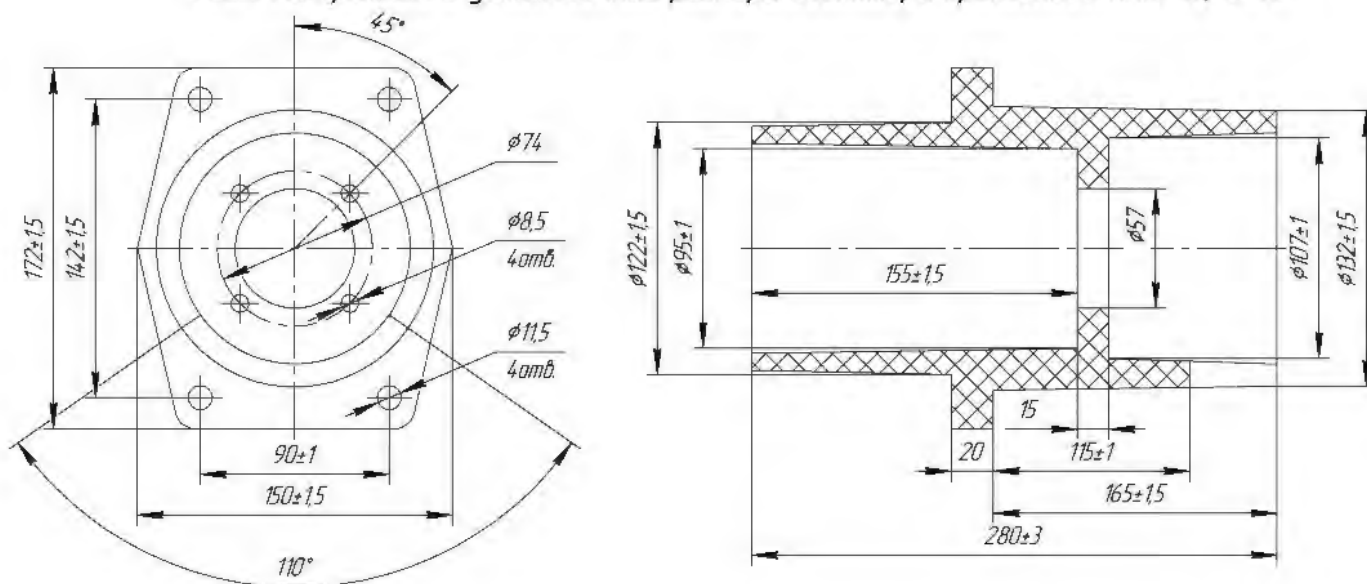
Габаритные и установочные размеры изолятора проходного ИПЛ-10/8 VI.
